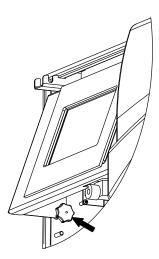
Position der Schrauben der Touchscreen-Baugruppe
